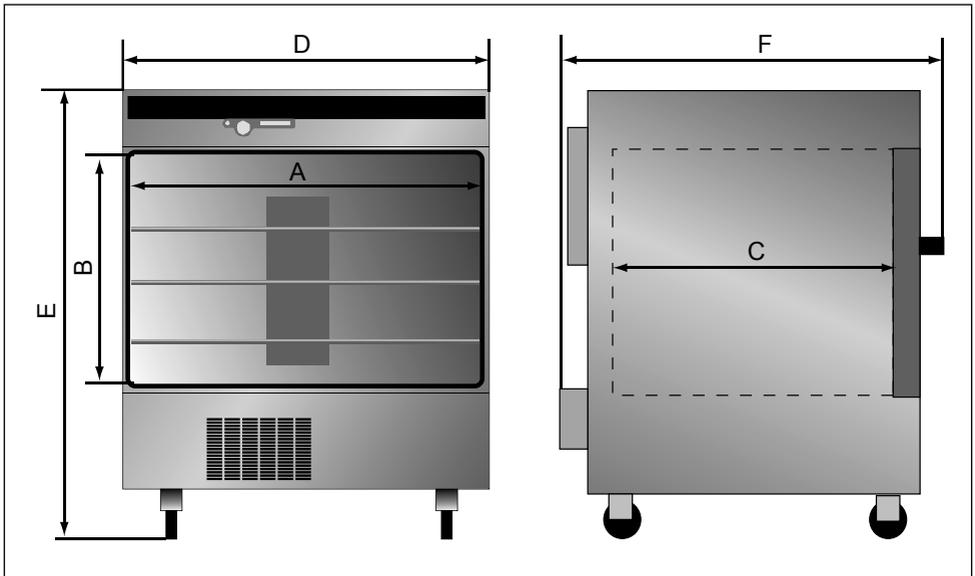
Abmessungen von Kühlbrutschränken ICH
